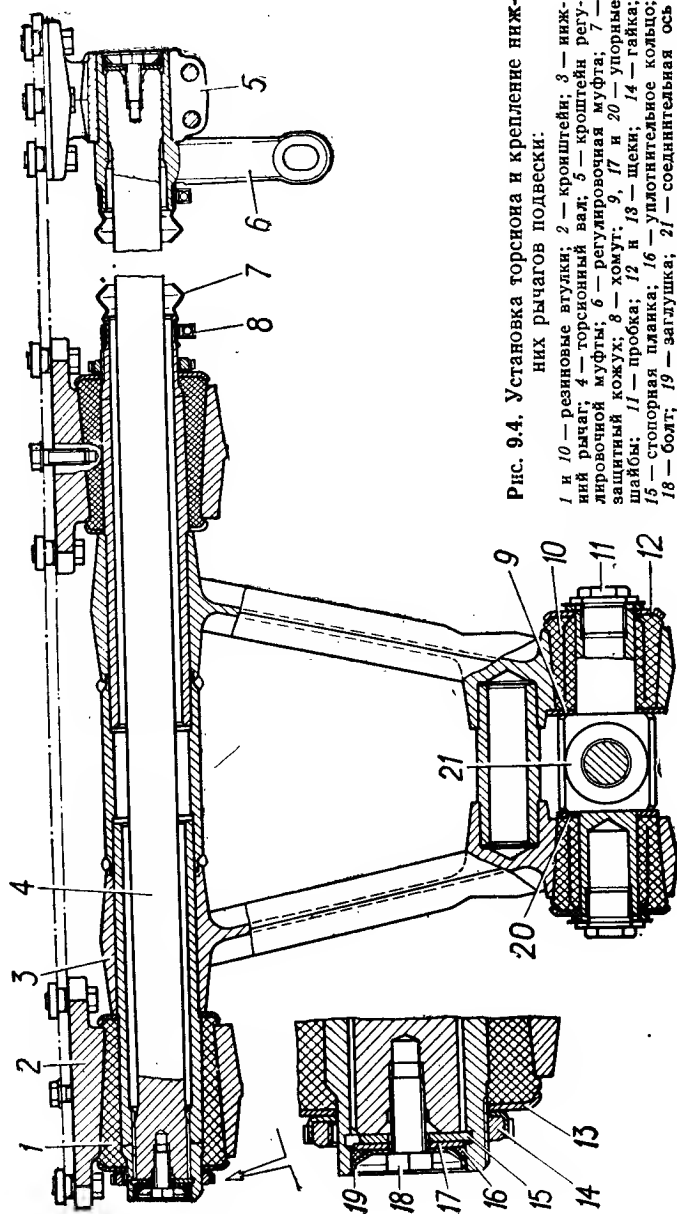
Установка торсиона и крепление нижних рычагов подвески:
